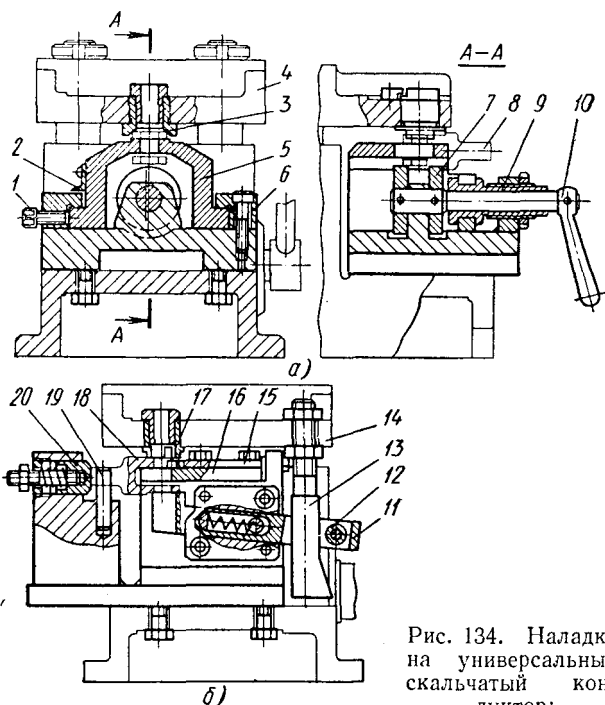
Наладка на универсальный скальчатый кондуктор:
